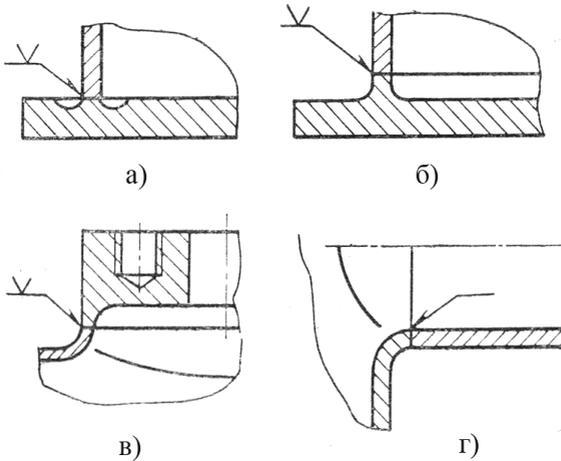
Конструктивное оформление сварных узлов деталей из высоколегированных сталей созданием равнотолщинности: а) обечайка и трубная решётка с проточками; б) обечайка и трубная решётка с выступом; в) обечайка и бобышка; г) обечайка и патрубок фланца
